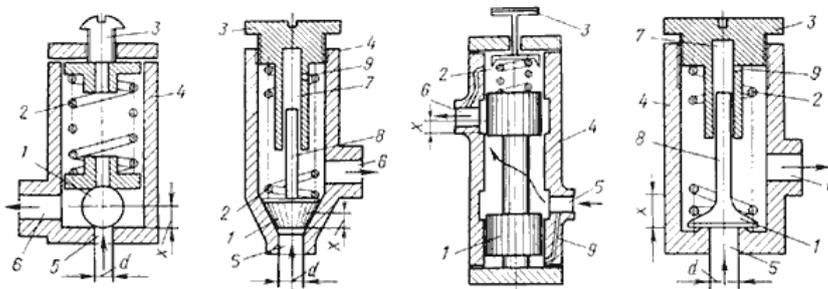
Принципиальные схемы напорных клапанов с запорно-регулирующими элементами: а - с шариковым; б - с конусным; в - с золотниковым; г - с тарельчатым.
